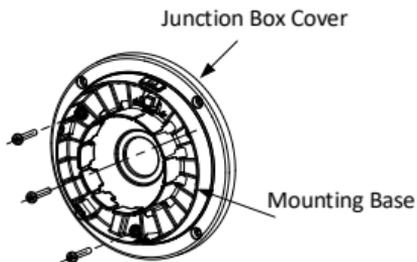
Fixe a Base de Montagem à Tampa da caixa de junção
